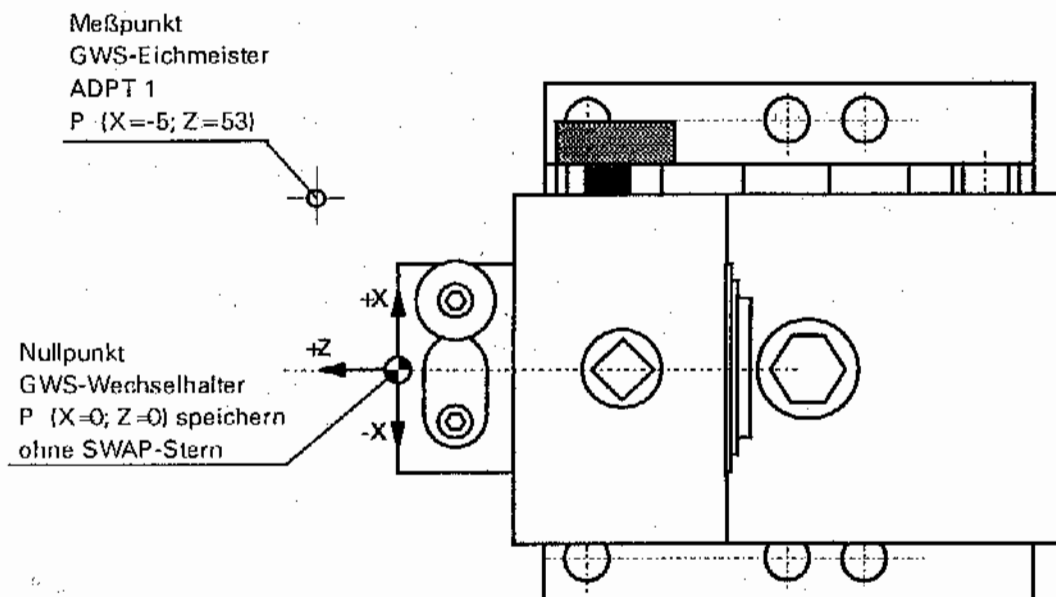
Nullpunkt am GWS-Wechseladapter für Pinolenwerkzeuge
